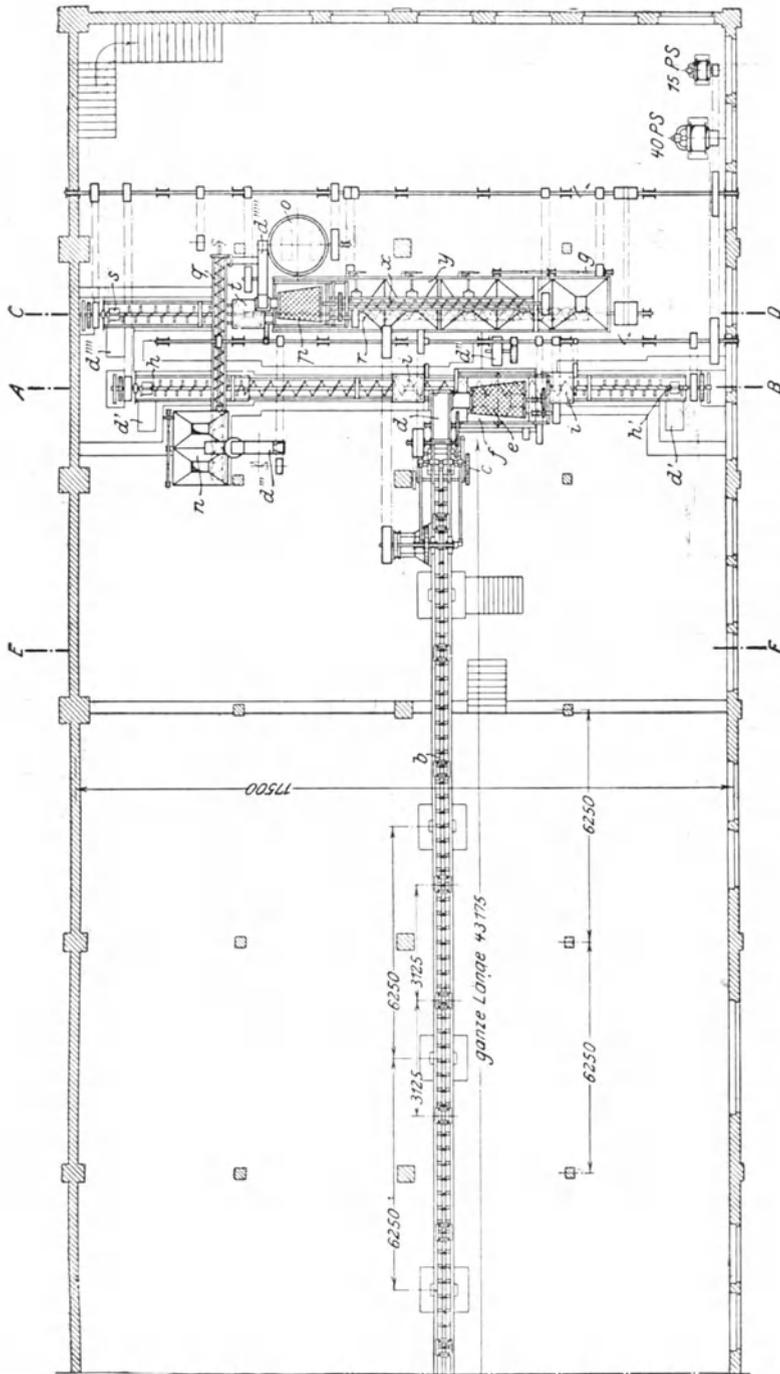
Formsandaufbereitungs- und Förderanlage, Grundriß des Kellergeschos.
